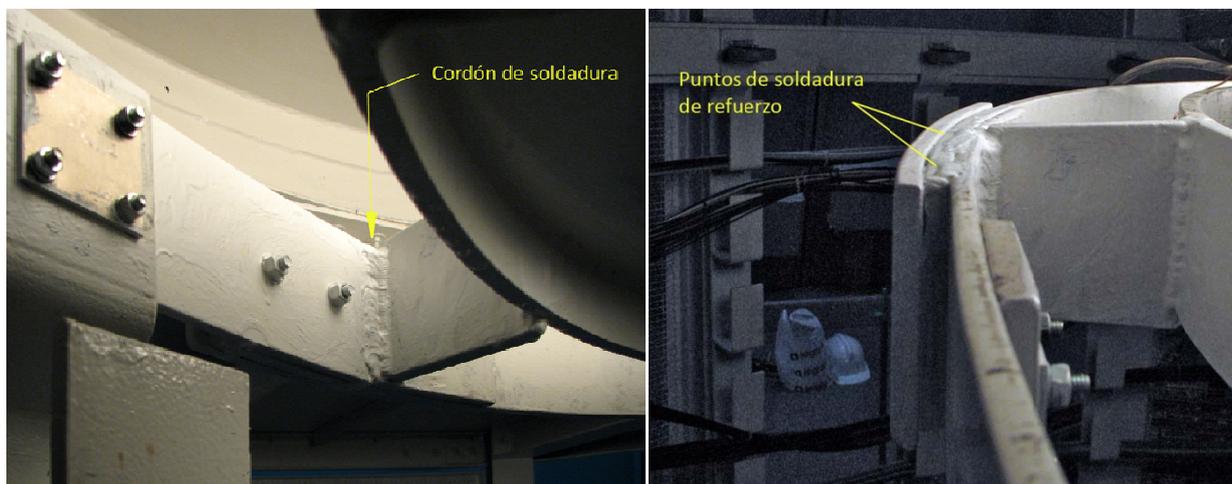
Soldadura de la pletina en la unión al tubo.
